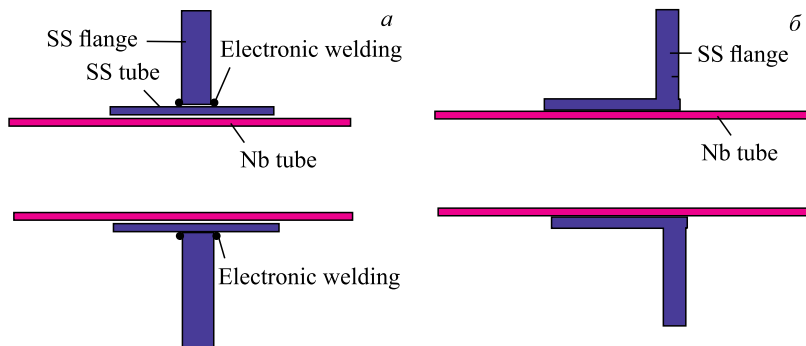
Схемы сварки Nb-трубок с нержавеющей фланцем
